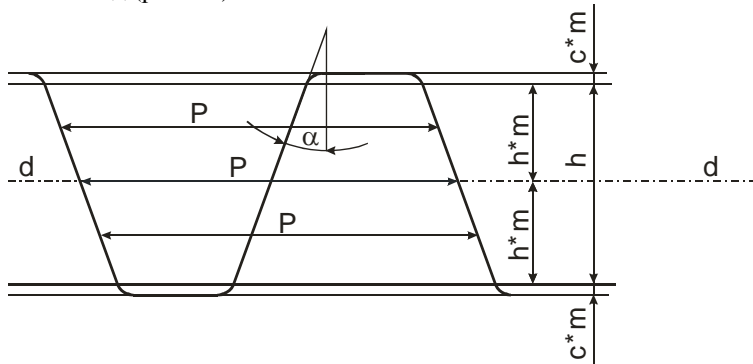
Профиль инструментальной гребенки или развертка инструментальной фрезы
